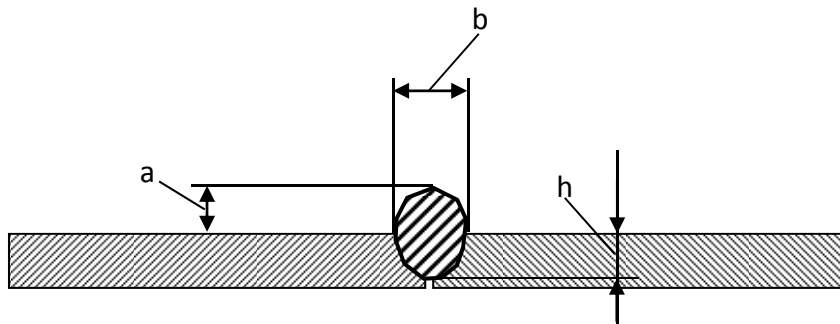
Схема розміщення: зварюваних пластин та параметрів зварного шва
